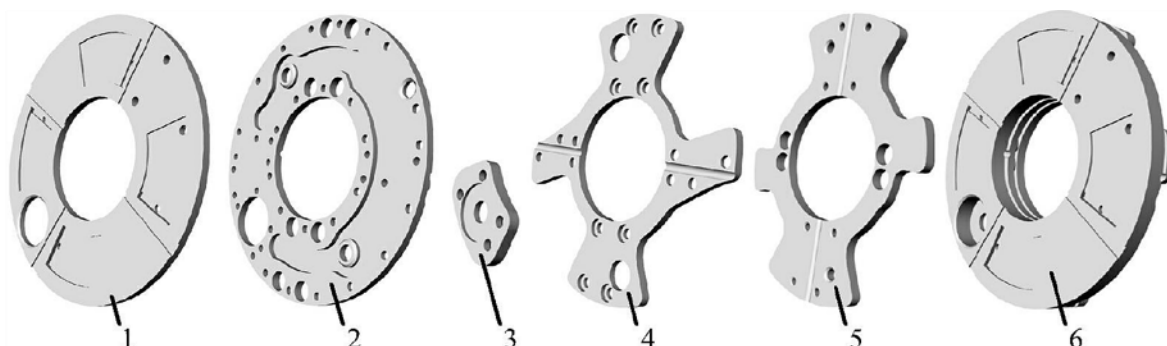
Основные детали и общий вид опытного образца гидростатодинамического подпятника со ступенью Рэля: 1 – верхний диск; 2 – нижний диск; 3 – крышка токовихревого датчика; 4 – верхняя крестовина; 5 – нижняя крестовина; 6 – опытный образец в сборе
